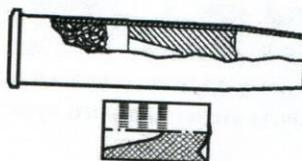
7,62-мм спортивный револьверный патрон В-1
